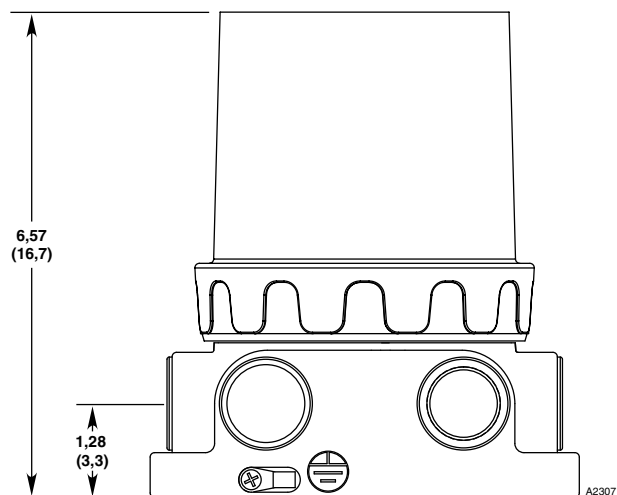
Dimensões da caixa de terminação em polegadas (cm)
